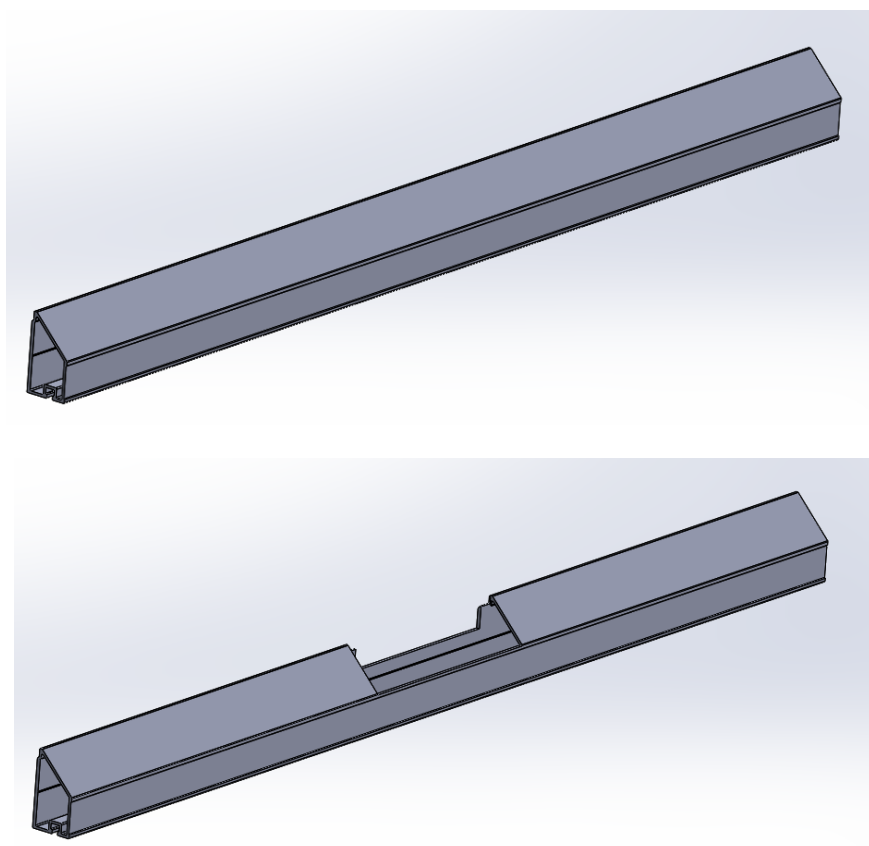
Perfil inferior y perfil inferior con cajeadado para portillón.
